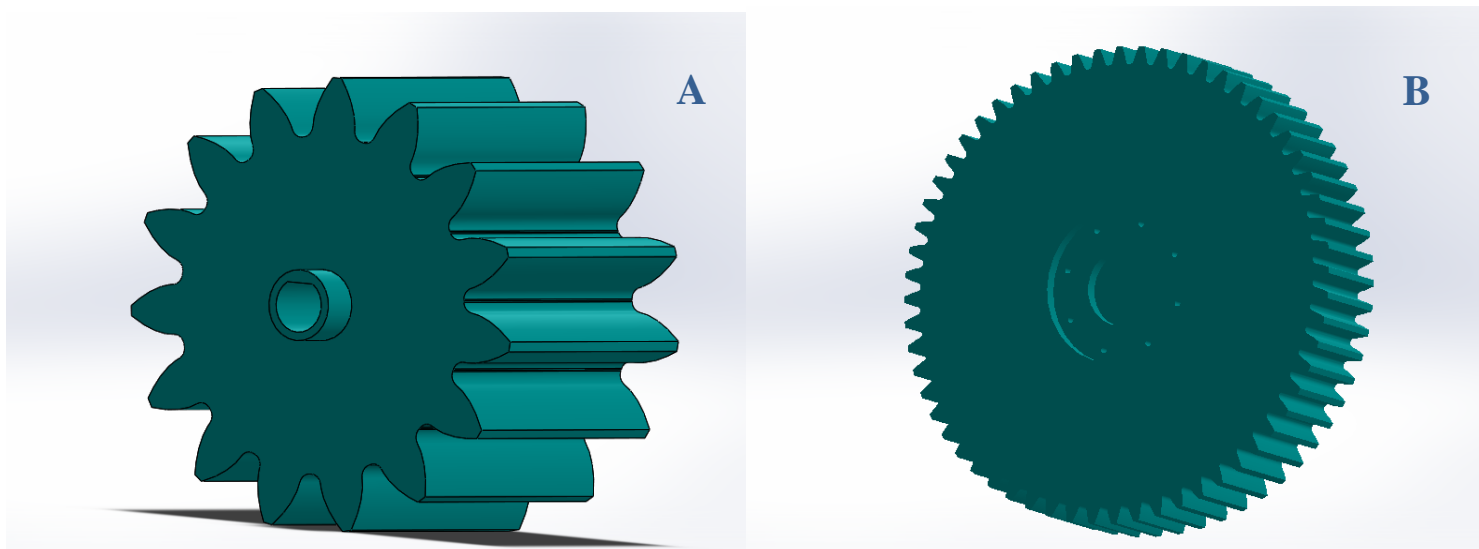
Engrenagem modificadas após dimensionamento A- pinhão B- roda (escalas diferentes)
